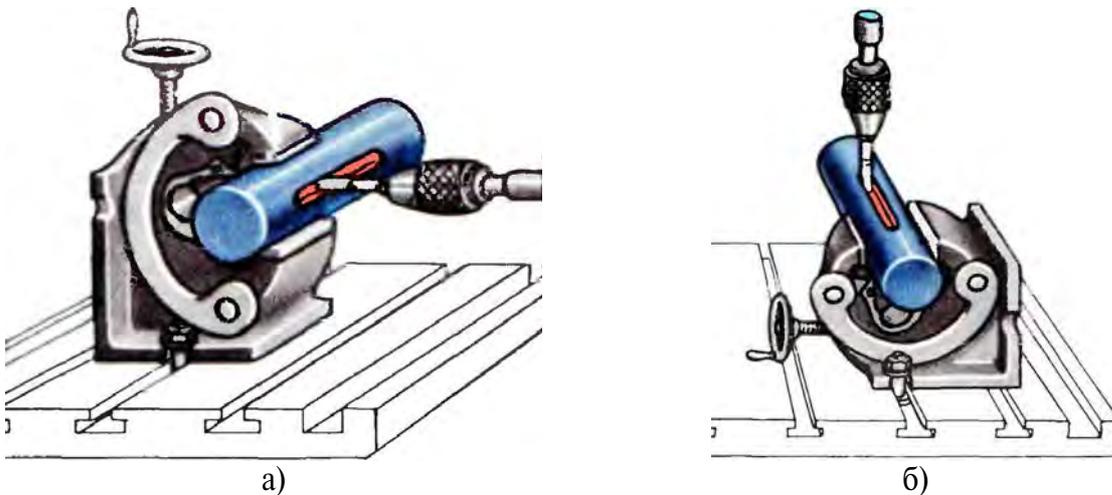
Фрезерование закрытых шпоночных пазов концевыми фрезами:
